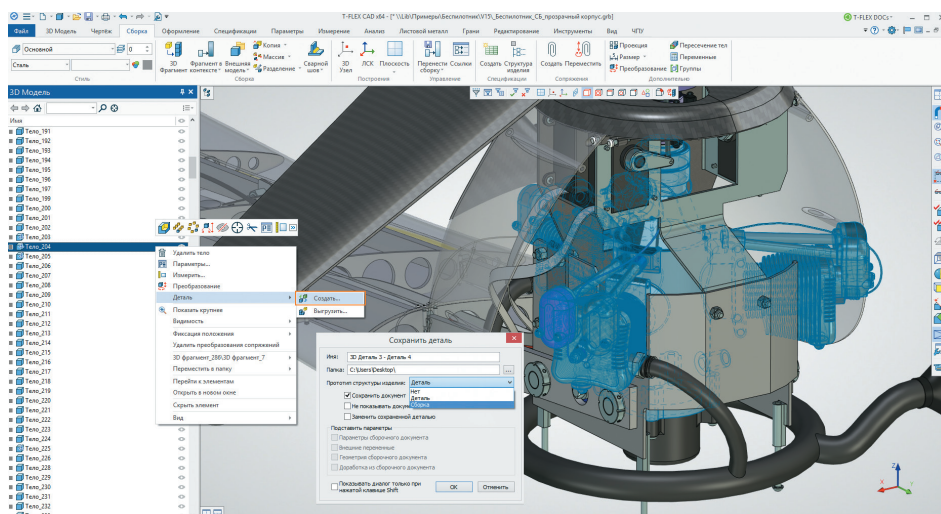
Выгрузка сборочной единицы из файла сборки с использованием новой команды создания детали
